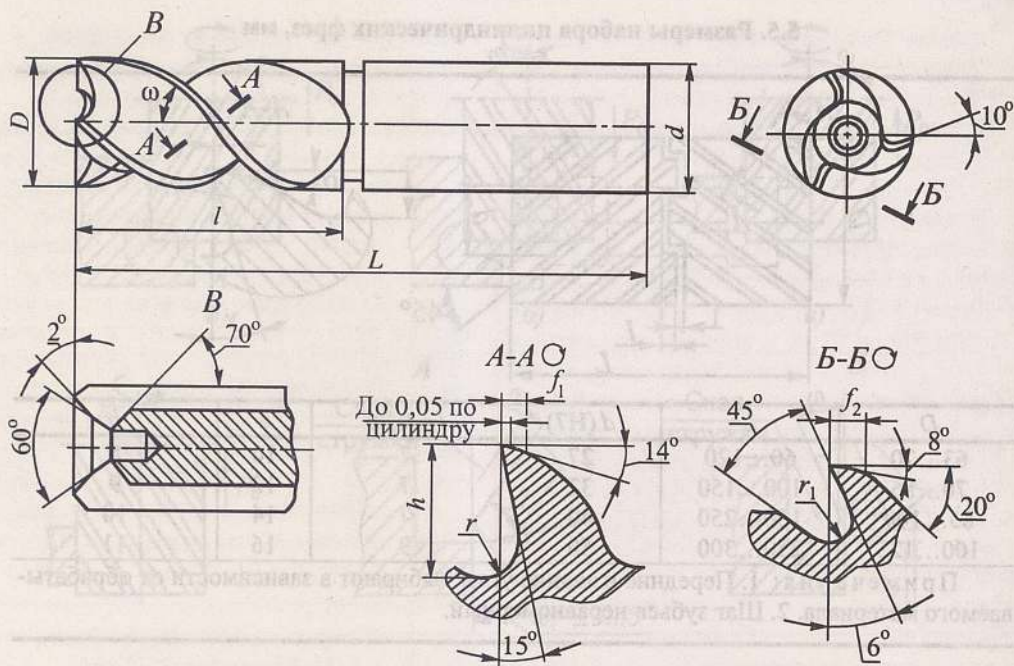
Конструкция и геометрические параметры концевой фрезы
